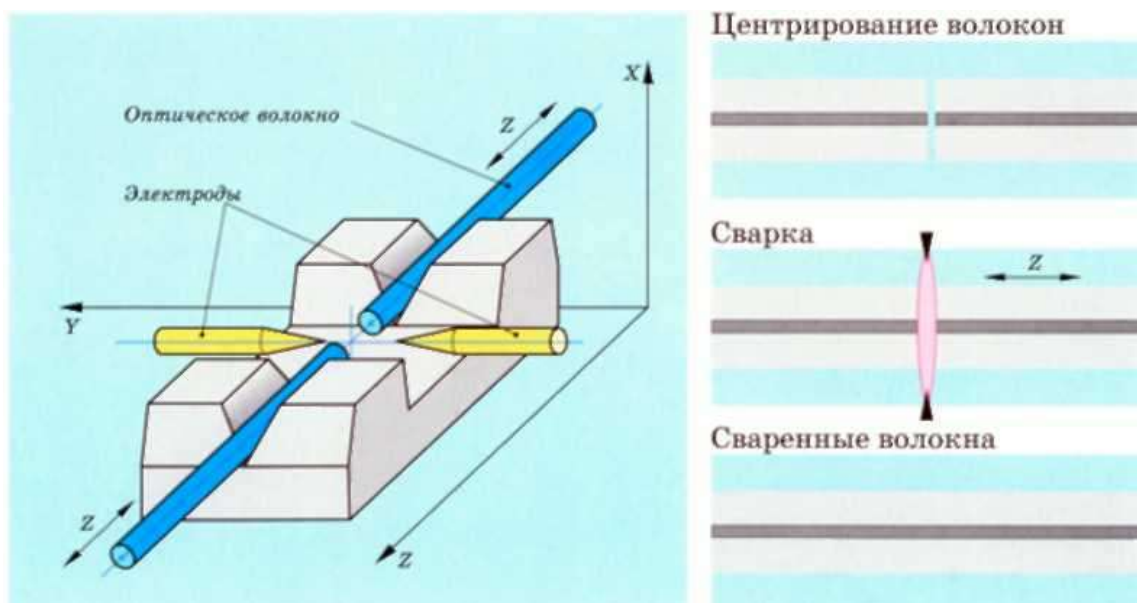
Принцип работы сварочного аппарата Fujikura FSM-18S
